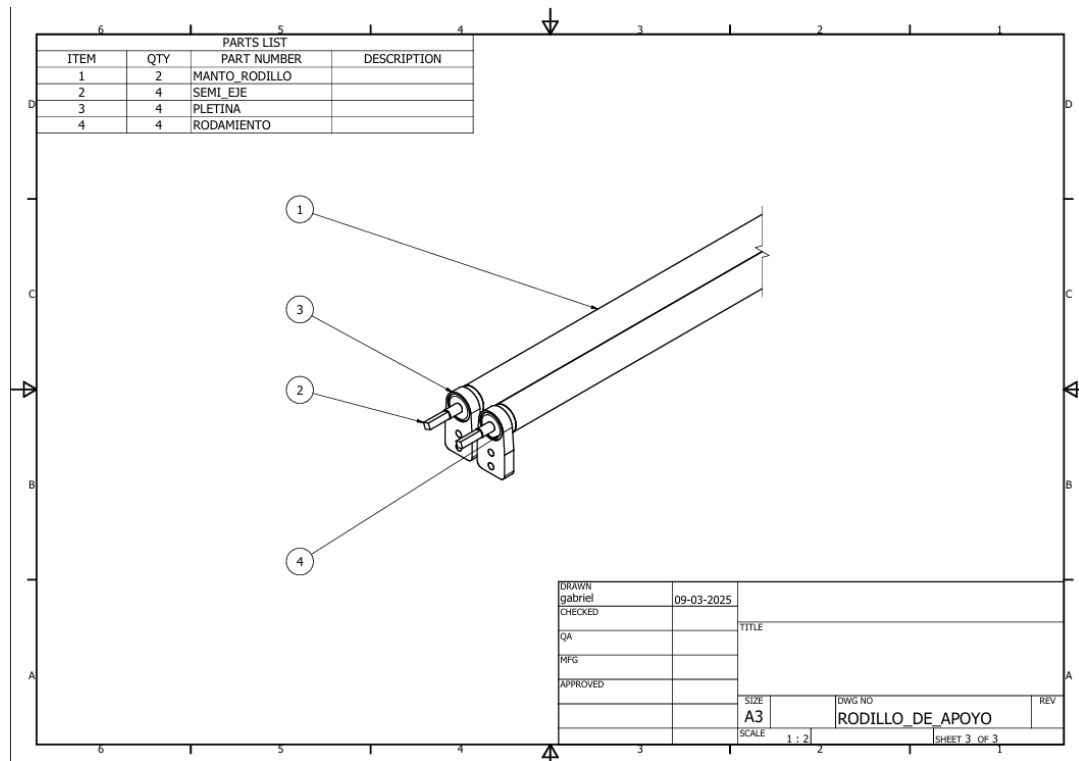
Plano que muestra los elementos pertenecientes al modulo de trabajo.
